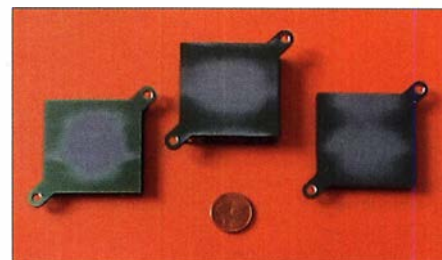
Kühlkörper nach der Bearbeitung; die beanspruchten Flächen sind gut erkennbar.
